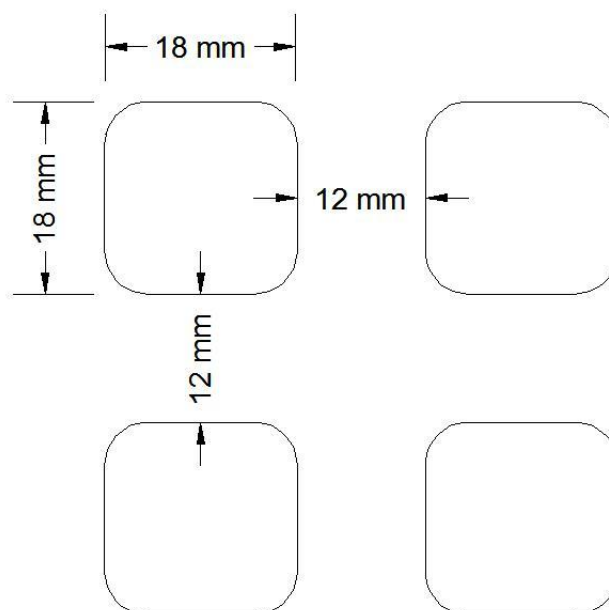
Pormenor da furação de um painel tipo CFQ.
